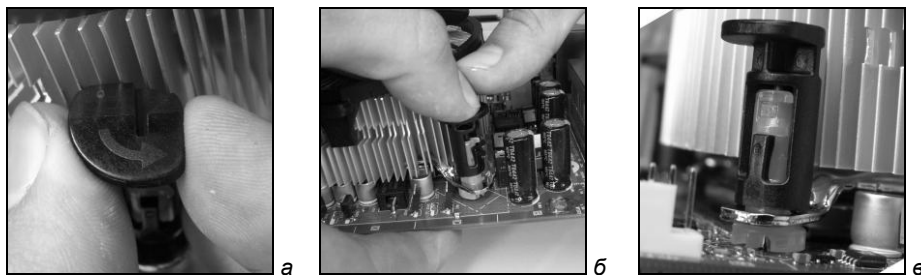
Установка кулера на процессор в корпусе LGA
